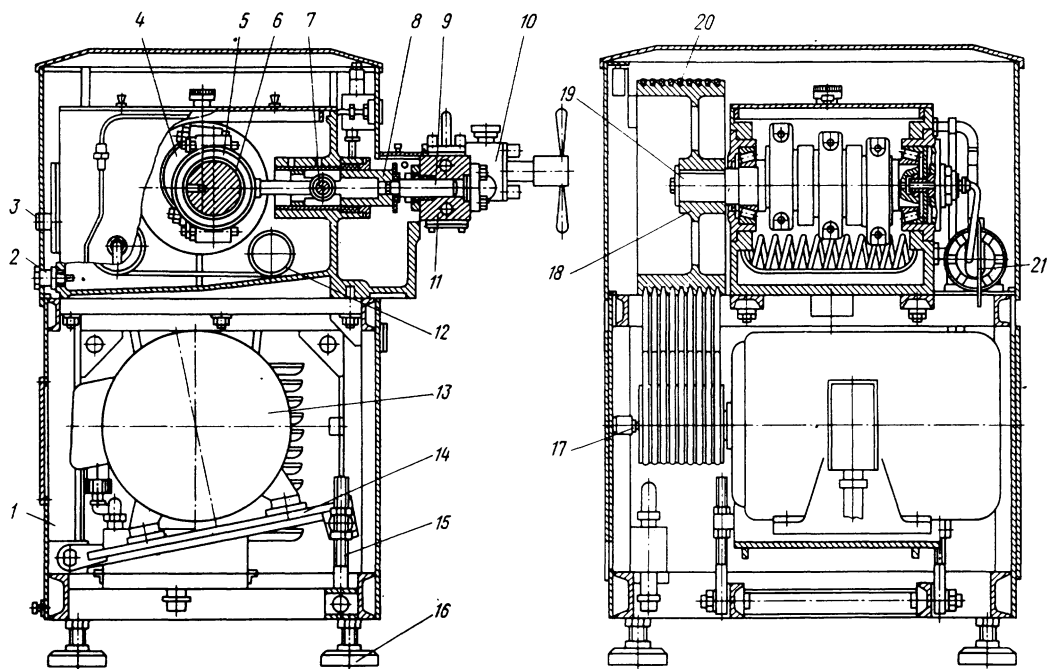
Загальний вид гомогенізатора А1-ОГМ
